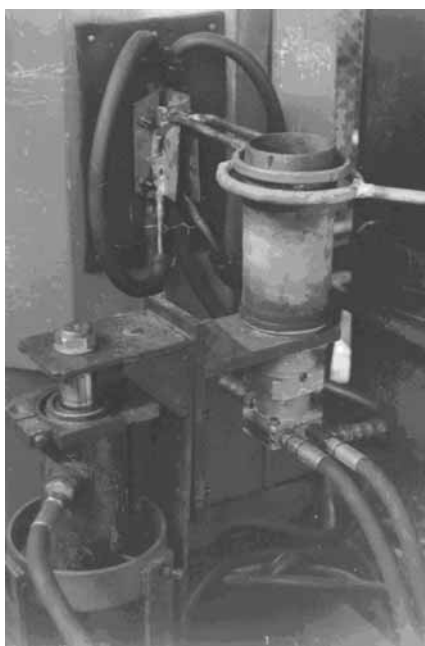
Общий вид установки ТПД гильзы цилиндра дизеля
